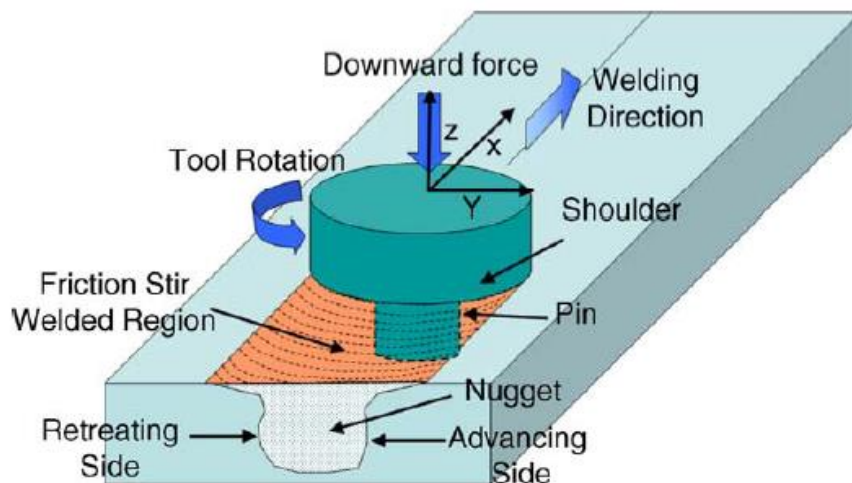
Desenho esquemático da ferramenta e do processo de solda por fricção.
